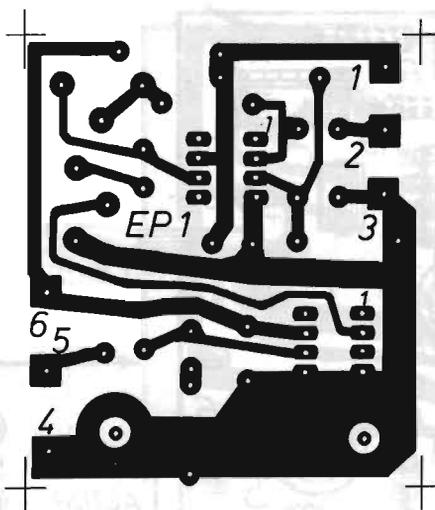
Disegno in grandezza reale del circuito stampato da riprodurre su una delle due facce di una basetta supporto di materiale isolante.
